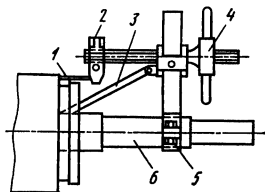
Приспособление для извлечения стержней из пазов ротора
